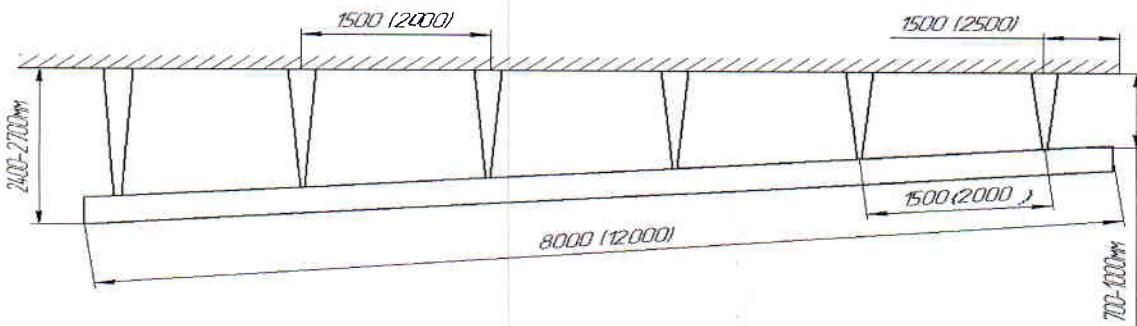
(б) Схема навески длинномерных сварных и тонкостенных заготовок
